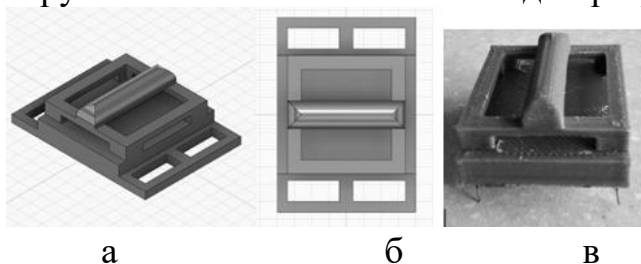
Графическое изображение фиксатора измерительного инструмента: а – вид в изометрии, б – вид сверху; в – образец изделия
